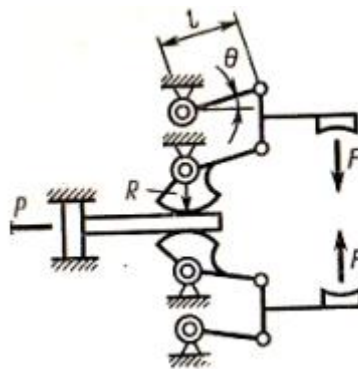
Кинематическая схема выбранного типа захватного Устройства
